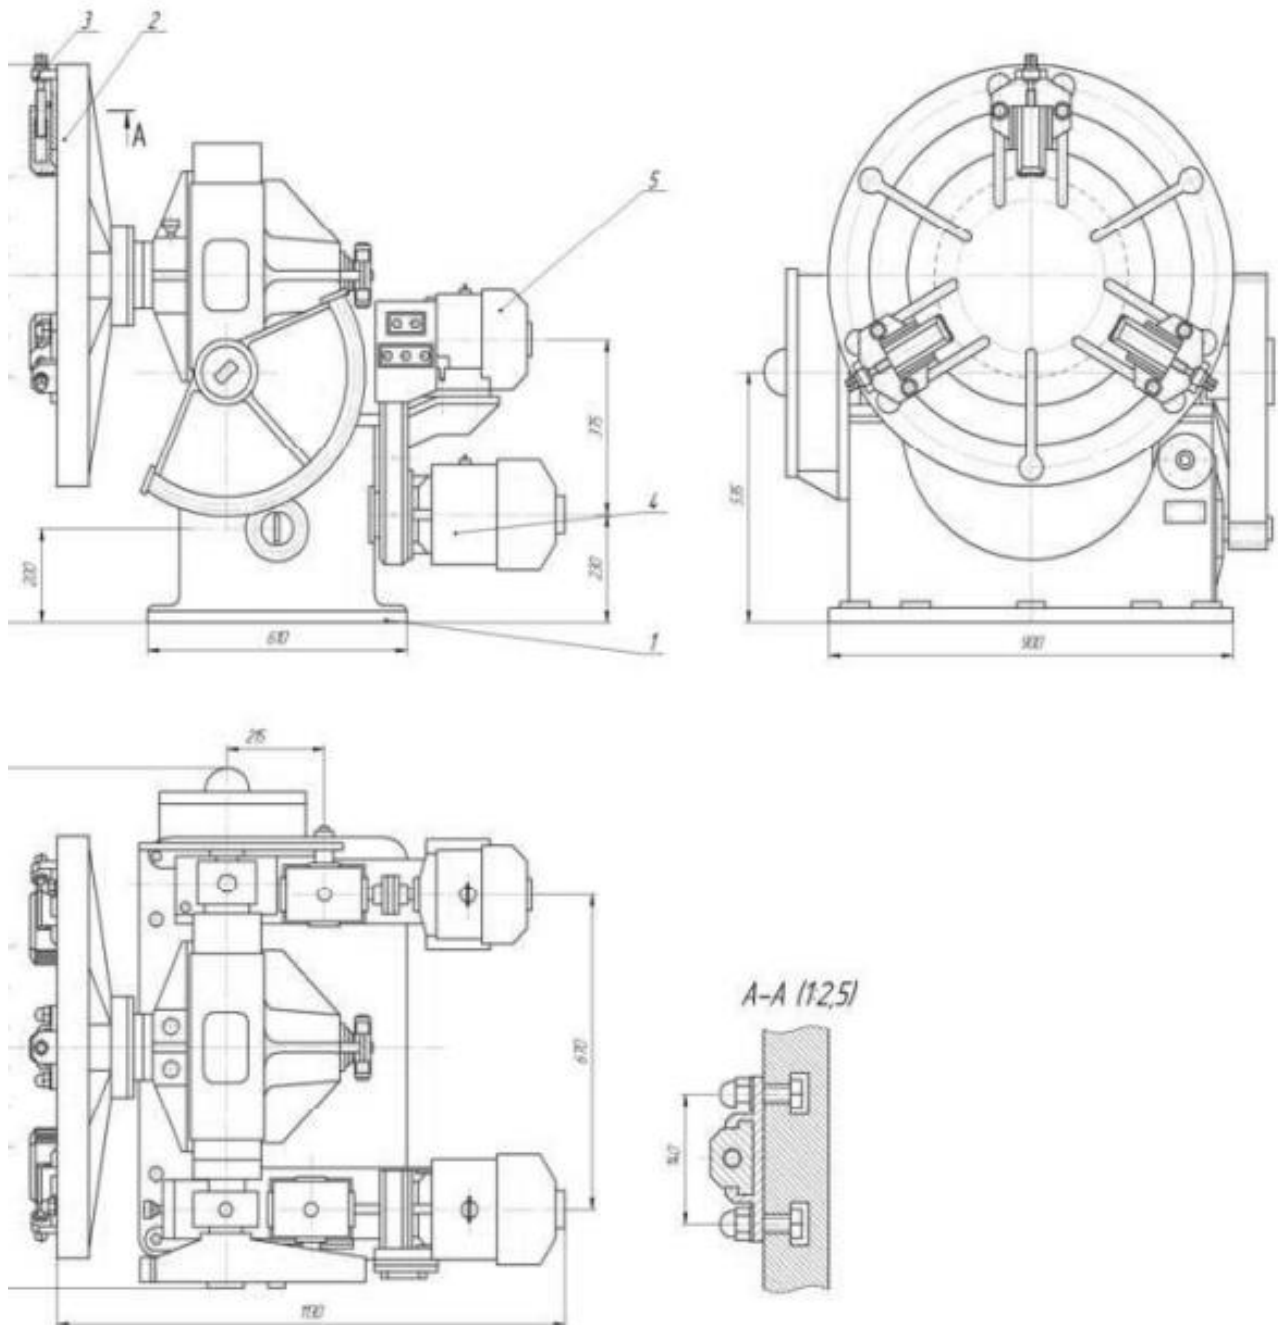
Обертач зварювальний: 1 – корпус; 2 – планшайба; 3 – рухомий кулачок; 4 – привод обертання; 5 – привод нахилу
